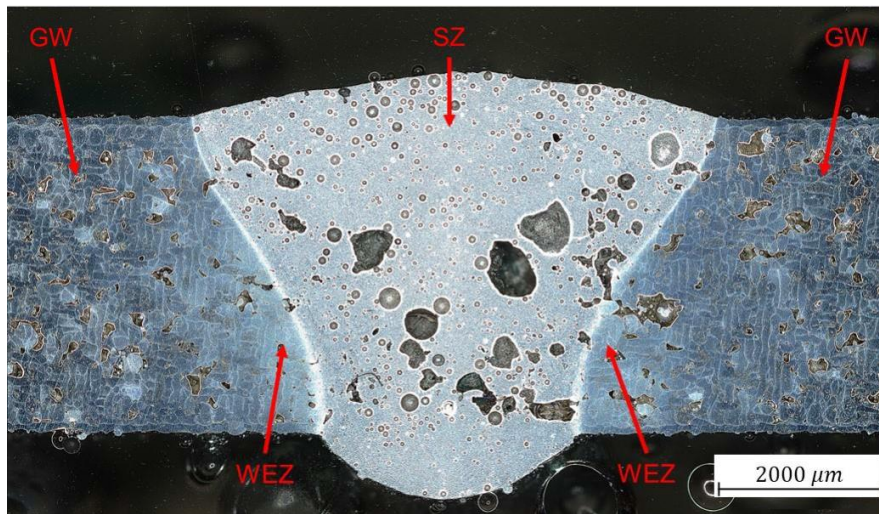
Gefüge im Bereich einer LBW-Schweißnaht
